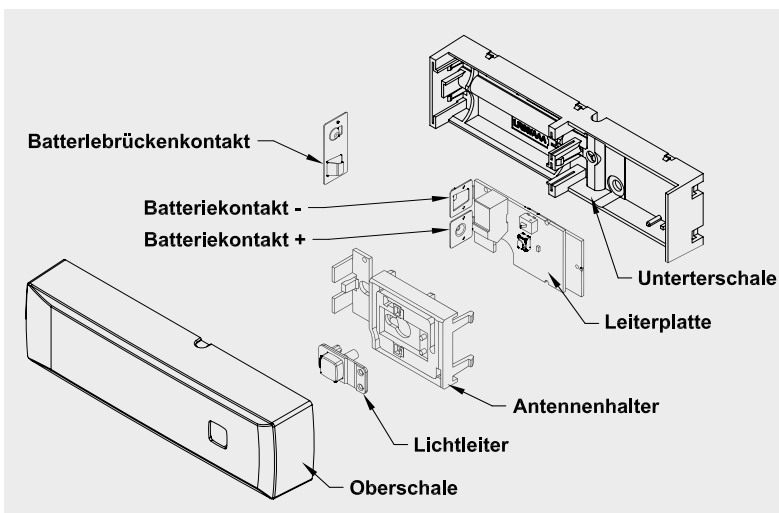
Die Explosionszeichnung zeigt die Lage aller Komponenten.
